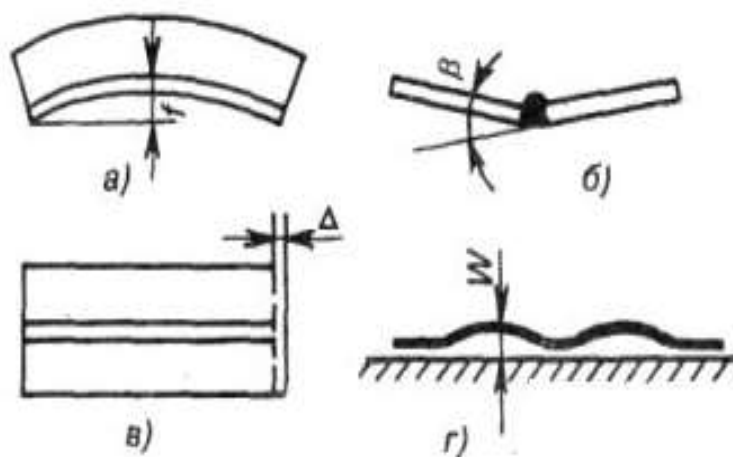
Виды перемещений при деформации сварных конструкций.
